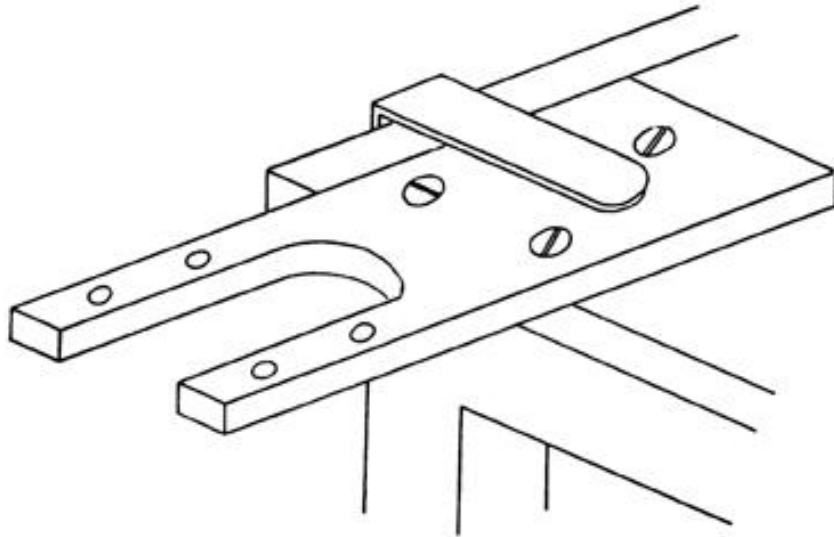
Bâti d'essai. Fixation par presse ou par vis sur une table ou sur un établi.
